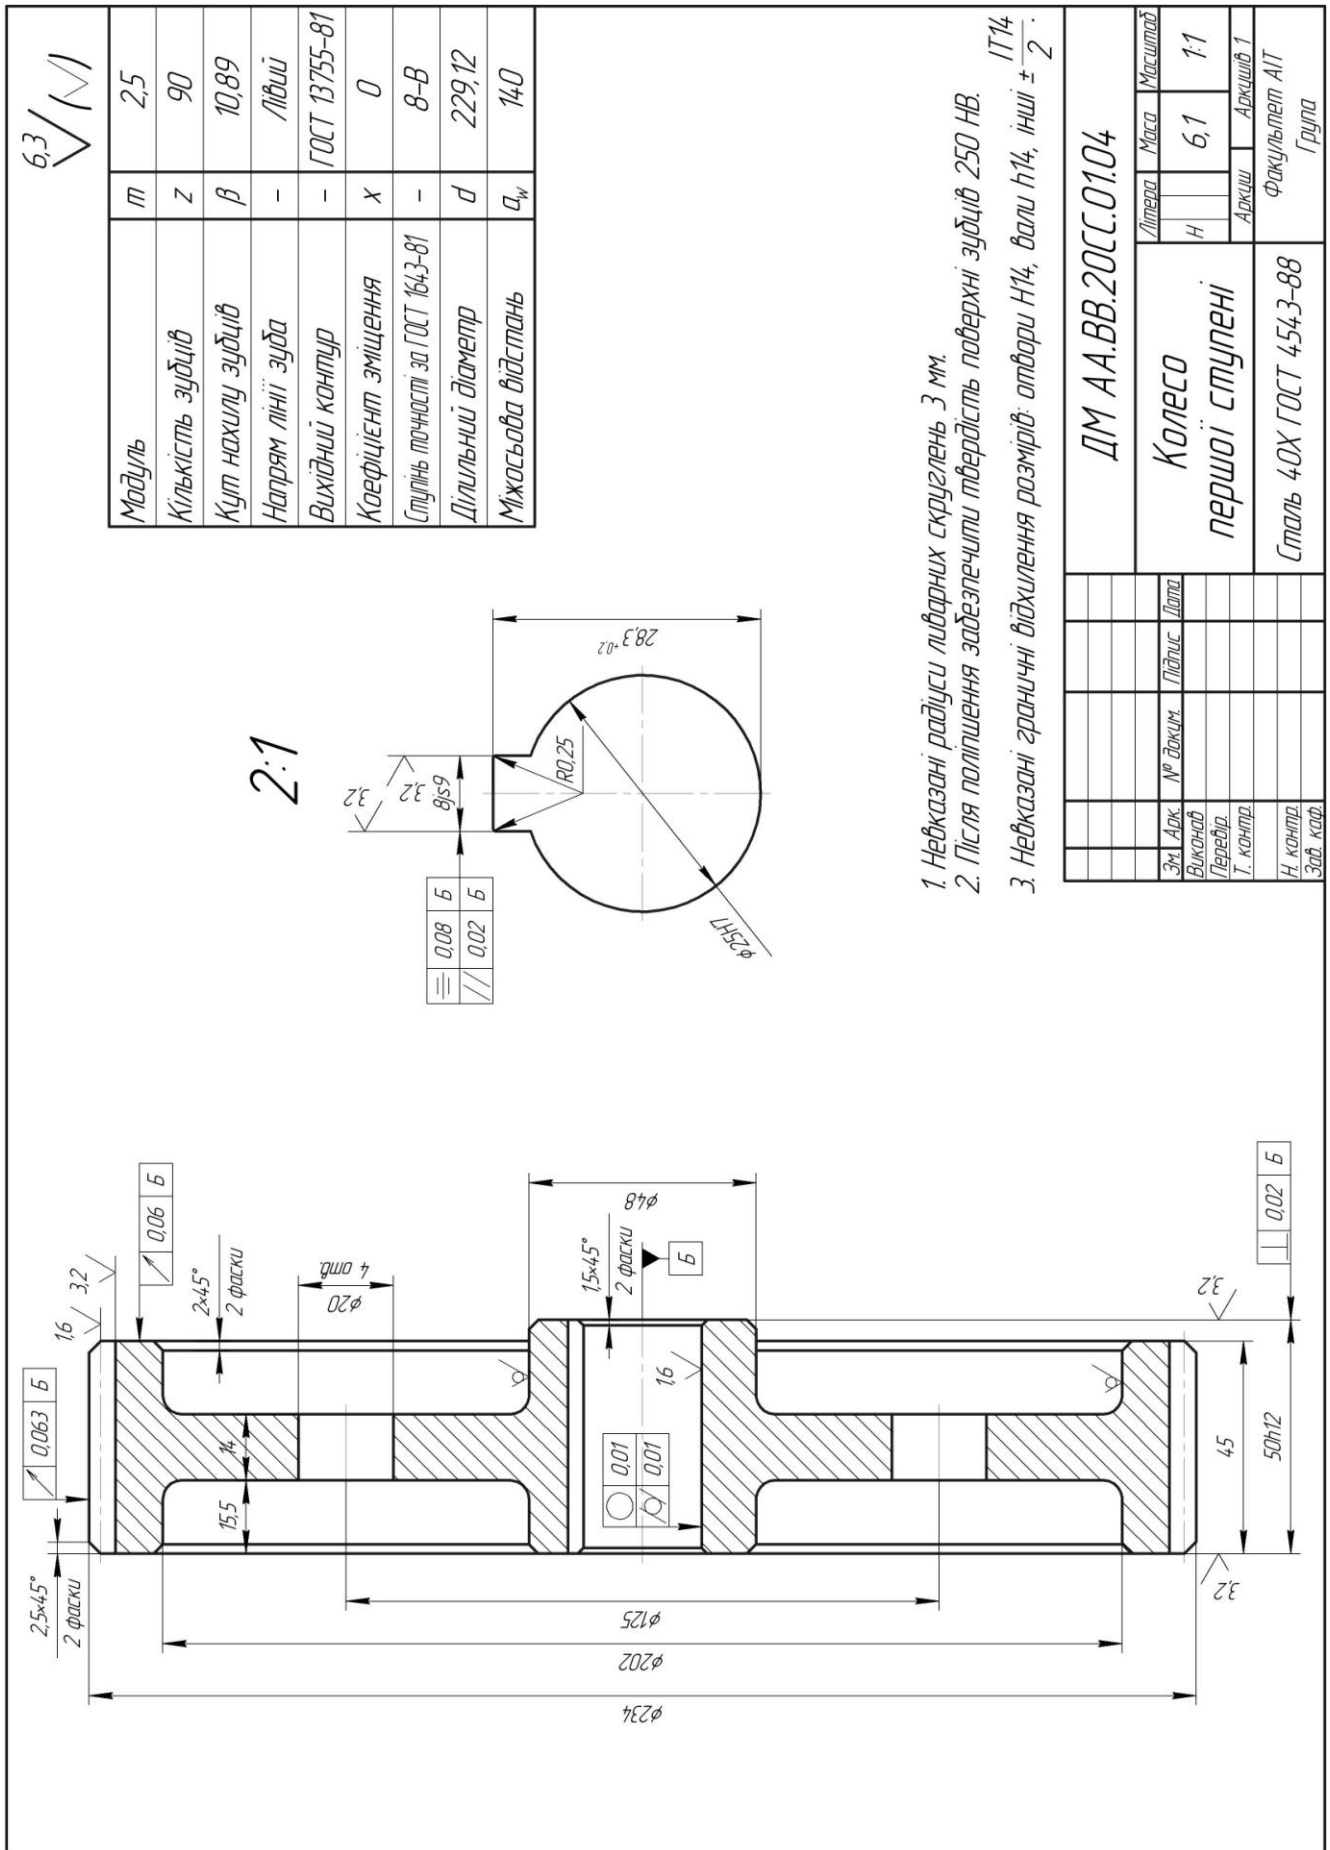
Приклад виконання робочого креслення циліндричного зубчастого колеса
